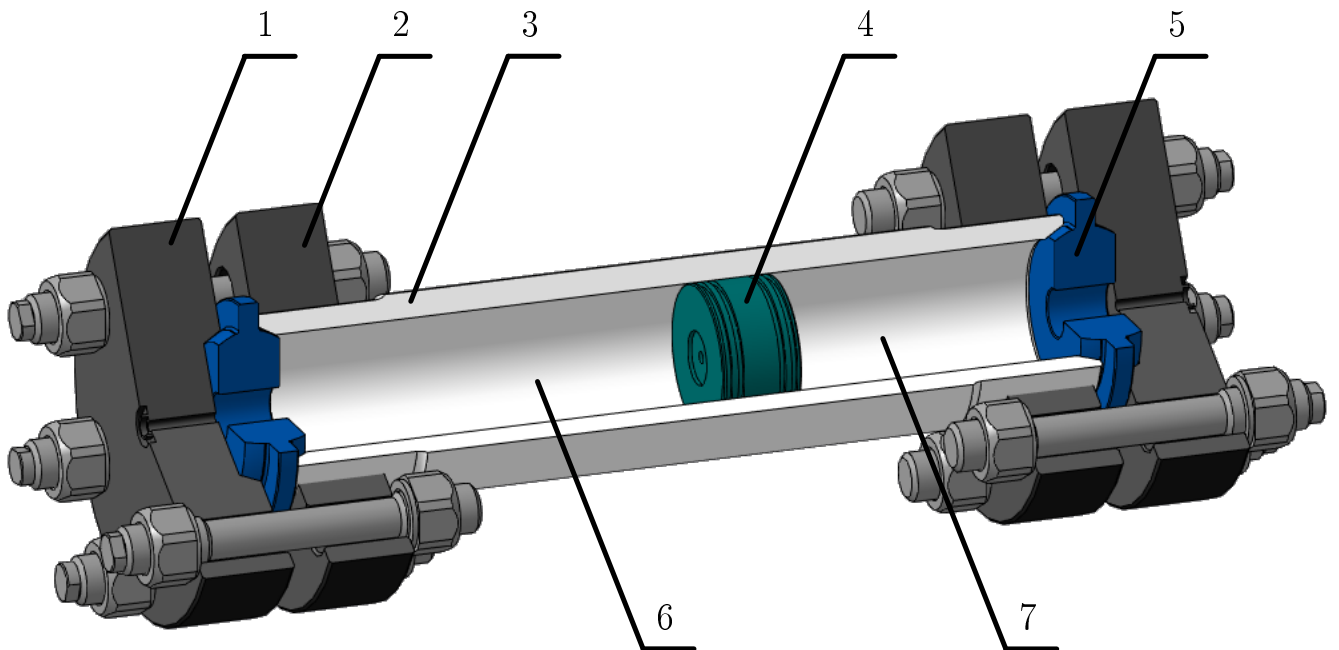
Модель разделительного цилиндра: 1 — глухой фланец; 2 — резьбовой фланец; 3 — корпус; 4 — поршень; 5 — линза; 6 — газовая полость; 7 — водяная полость
